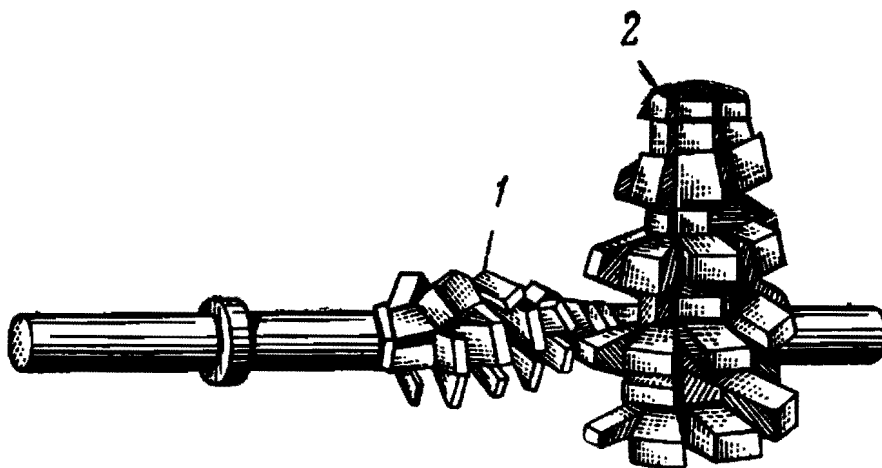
Червячные фрезы для нарезания червячных колес методом тангенциальной подачи
